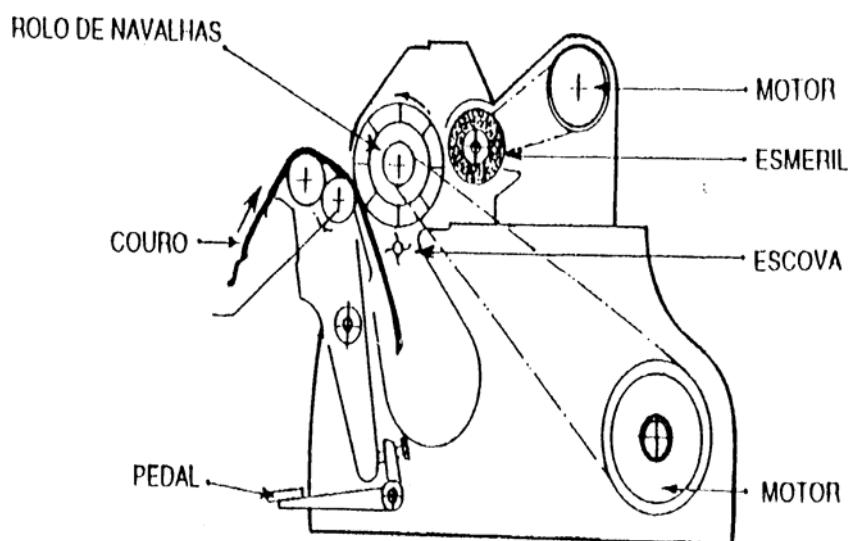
Máquina de rebaixar ou rebaixadeira.
